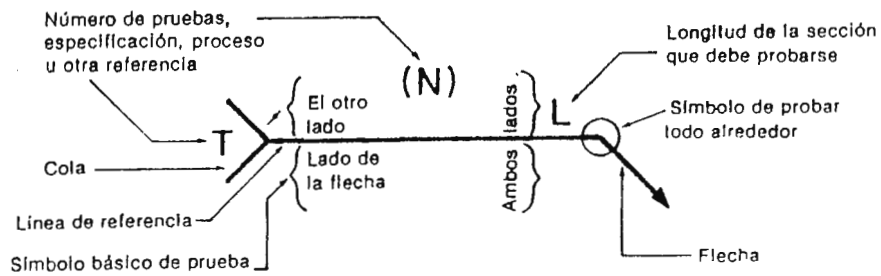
Símbolo de ensayo de soldadura
